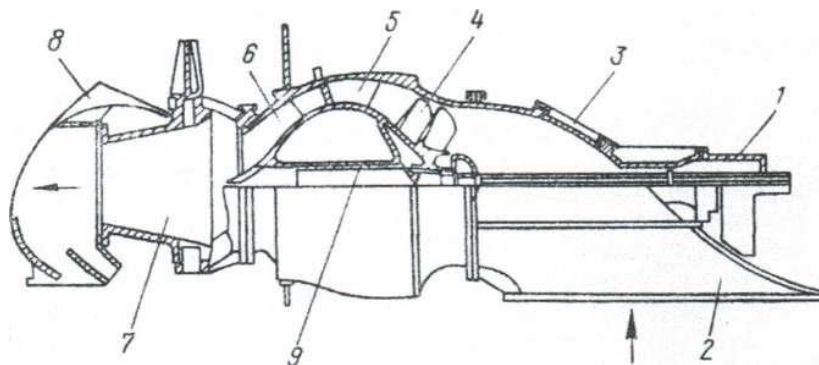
Водомётный движитель малого хода корабля класса РНМ (США). 1- узел уплотнения и подшипника; 2 - водозаборное отверстие; 3 - смотровой люк; 4 - рабочее колесо; 5 - спрямляющий аппарат; 6 - сопло; 7 - поворотное сопло; 8 - заслонка реверсивного устройства; 9 - подшипник скольжения
